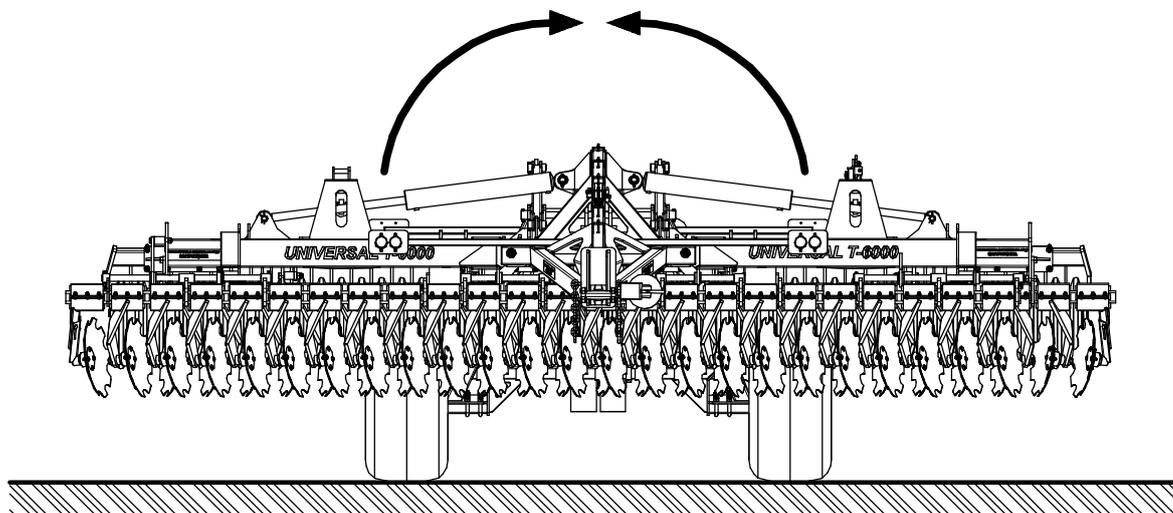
Перевод агрегата в транспортное положение. ДПМ"Универсал" / "Универсал Т" (впереди)
